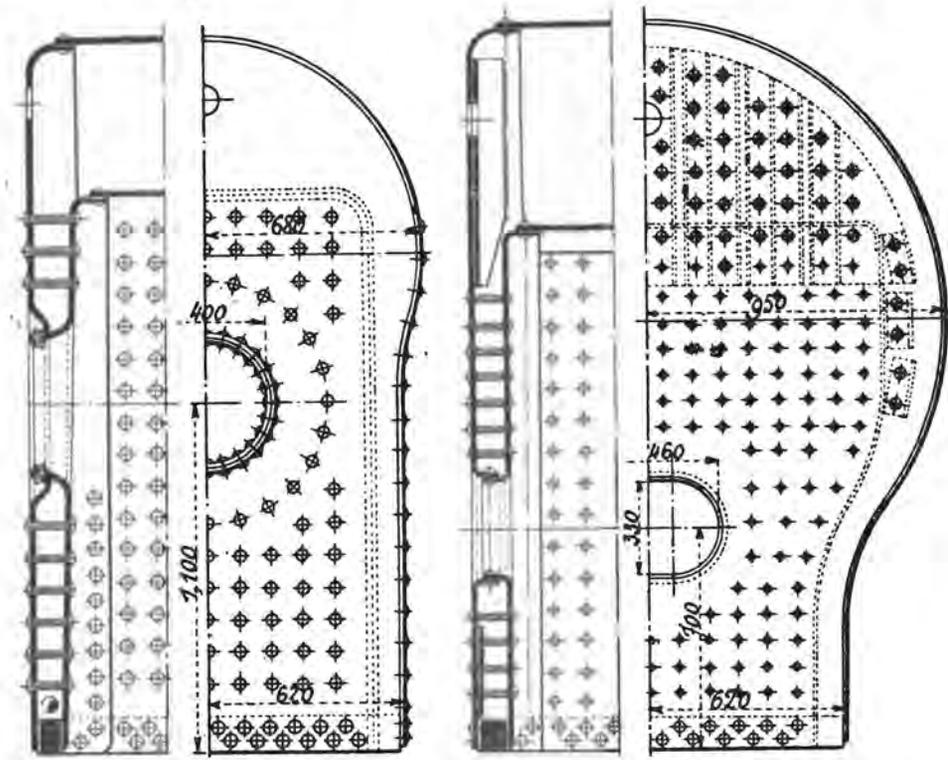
Dispositions américaines ayant pour but de remplacer, par l'assemblage de pinces embouties, le cadre de la porte du foyer.
